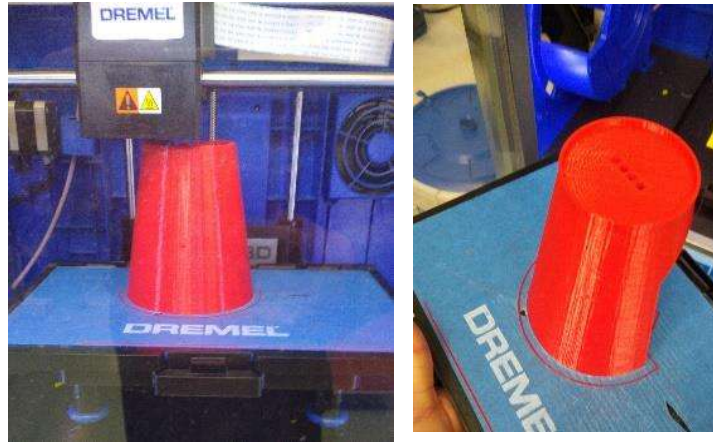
Etapa final de la impresión del soporte con nuevo diseño
